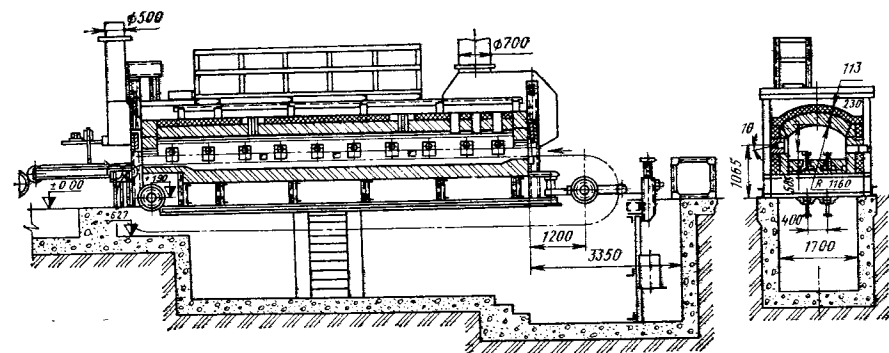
Конвейерная печь с подподовым конвейером для нагрева перед штамповкой листовой заготовки [напряженность пода 200—400 кг/(м²·ч)]
